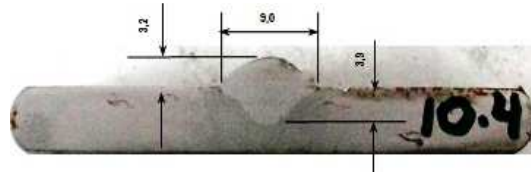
Macrografias com altura do reforço (r), largura do cordão de solda (b) e a penetração das soldas com CO₂.
